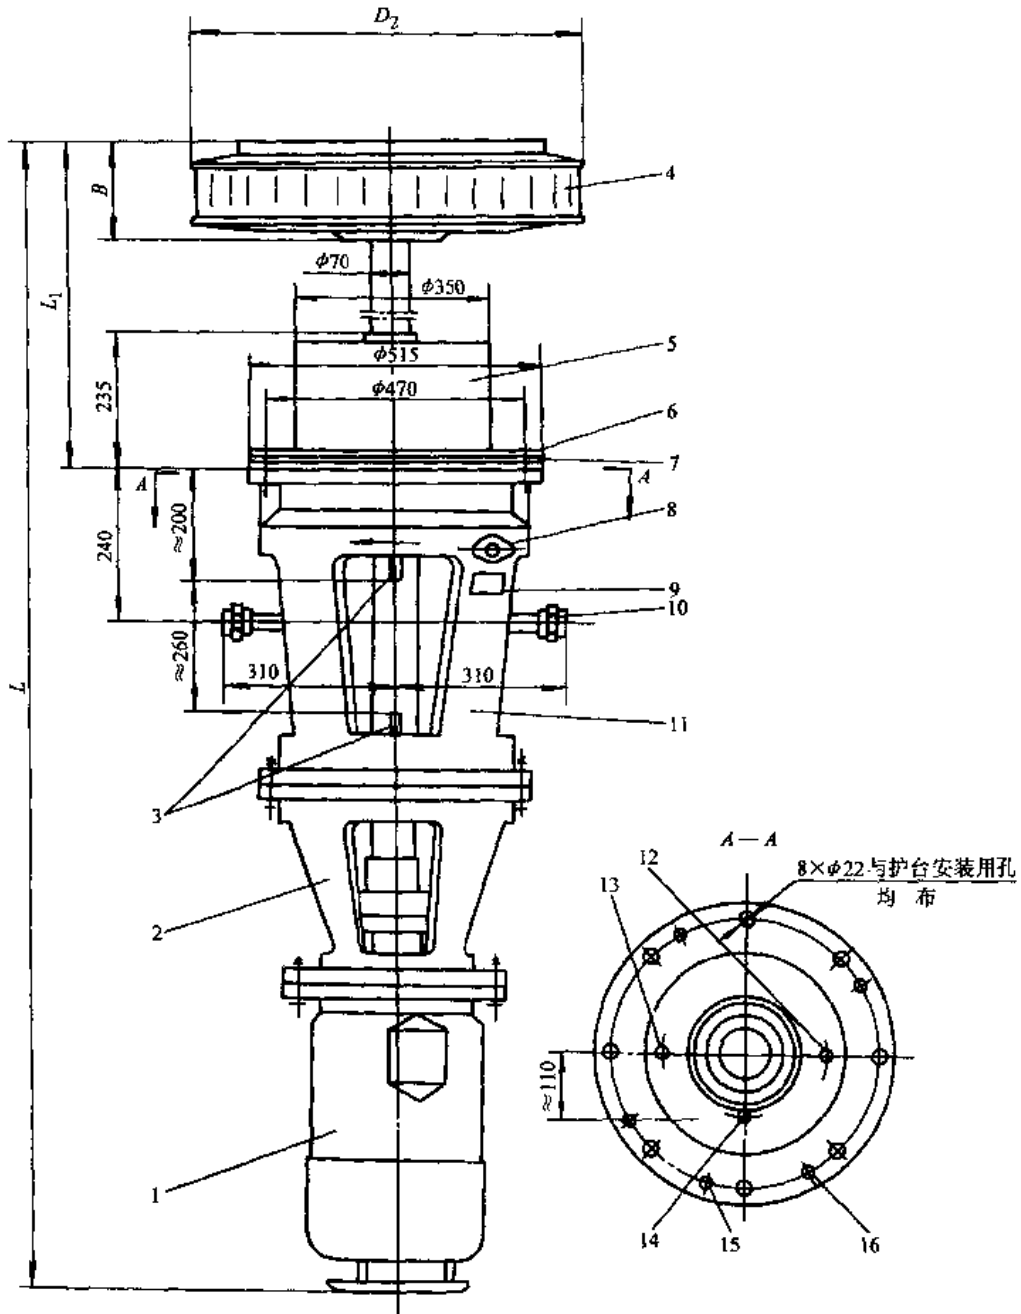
W4--80-11 No.5,6 装配图及外形尺寸
